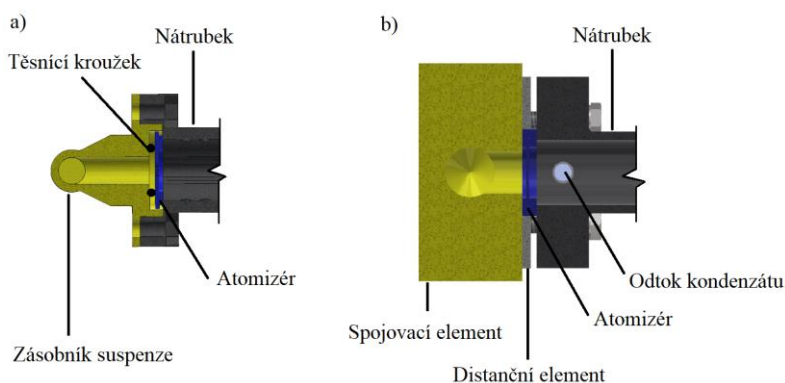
a) Řez původní pistolí, b) Řez novou pistolí
